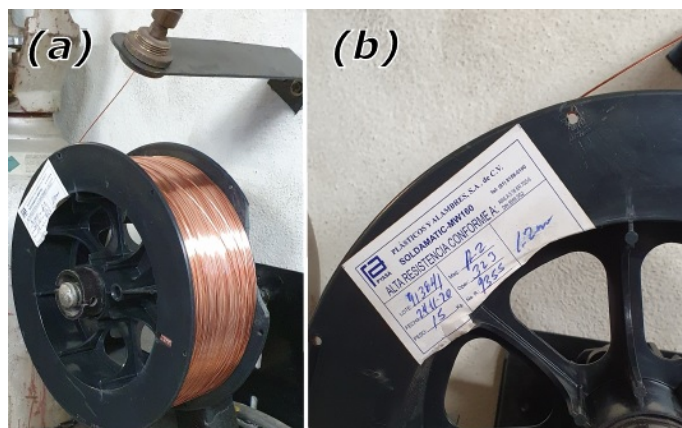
(a) Alambre de soldadura Soldamatic MW160 utilizado para el estudio. (b) Identificador del alambre.
